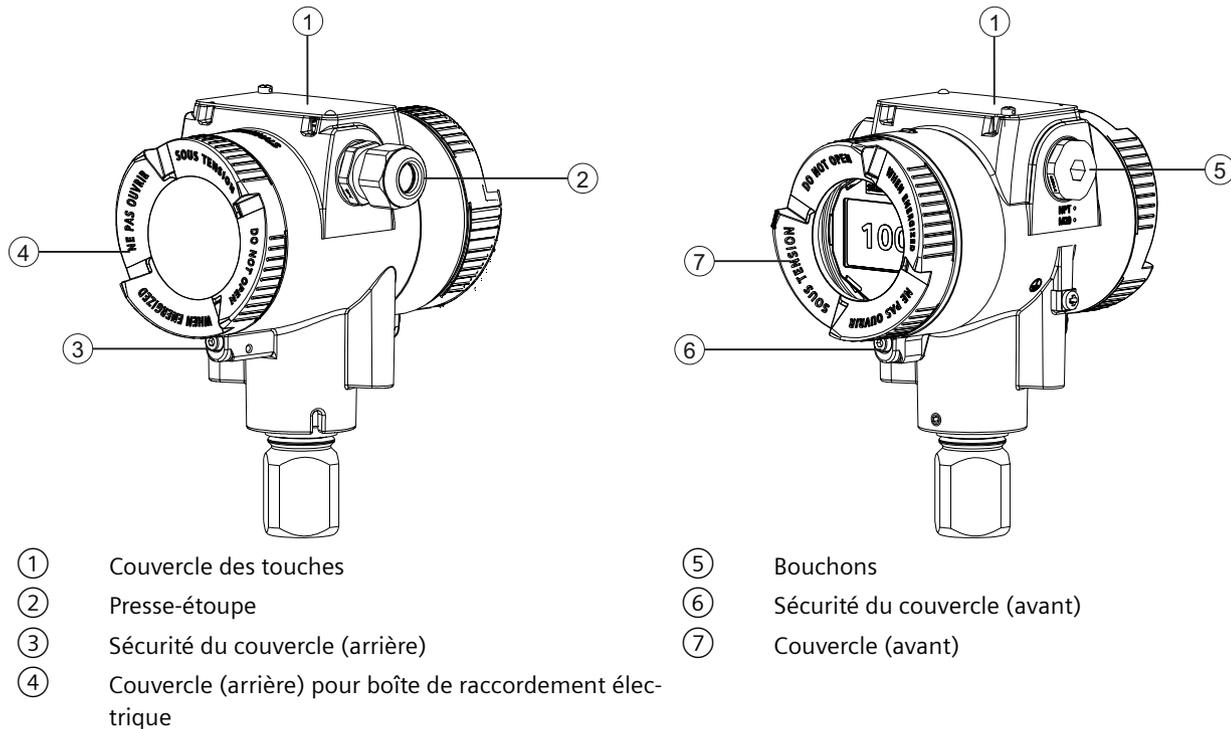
Vue du transmetteur de pression : à gauche : vue arrière, à droite : vue de face
